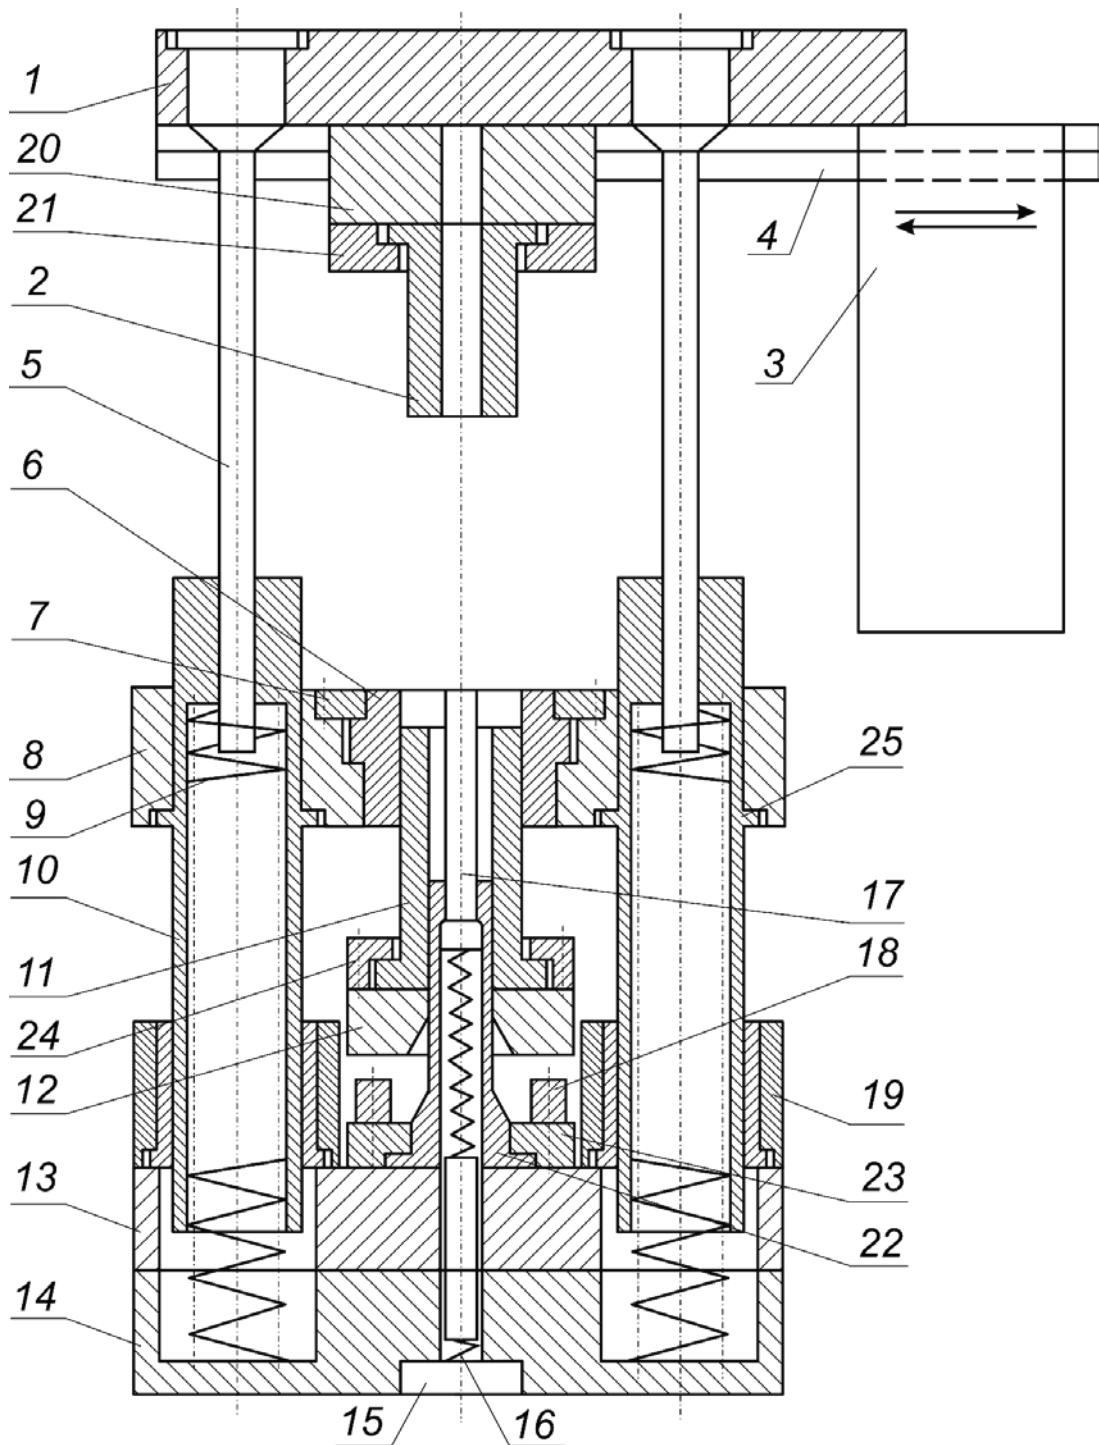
Общий вид пресс-формы: 1 – верхняя плита; 2 – пуансон верхний; 3 – толкатель; 4 – направляющие; 5 – колонки; 6 – матрица; 7 – крышка матрицы; 8 – плита подвижная; 9 – пружина; 10 – комбинированные колонки втулки; 11 – пуансон; 12 – подпружиненная плита; 13 – промежуточная плита; 14 – нижняя плита; 15 – пробка; 16 – пружина; 17 – центральный стержень; 18 – вилка; 19 – прижимная плита; 20 – пуансонодержатель; 21 – крышка верхняя; 22 – направляющая пуансона; 23 – прижим направляющей; 24 – прижим пуансона; 25 – направляющая втулка
